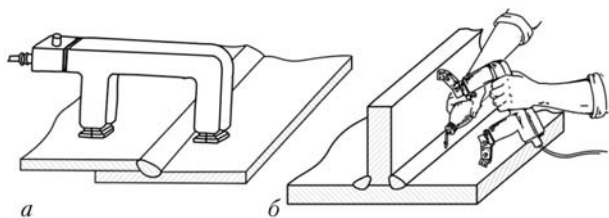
Схема намагничивания сварных соединений с помощью приставного электромагнита: а — нахлесточного шва; б — уторного шва
